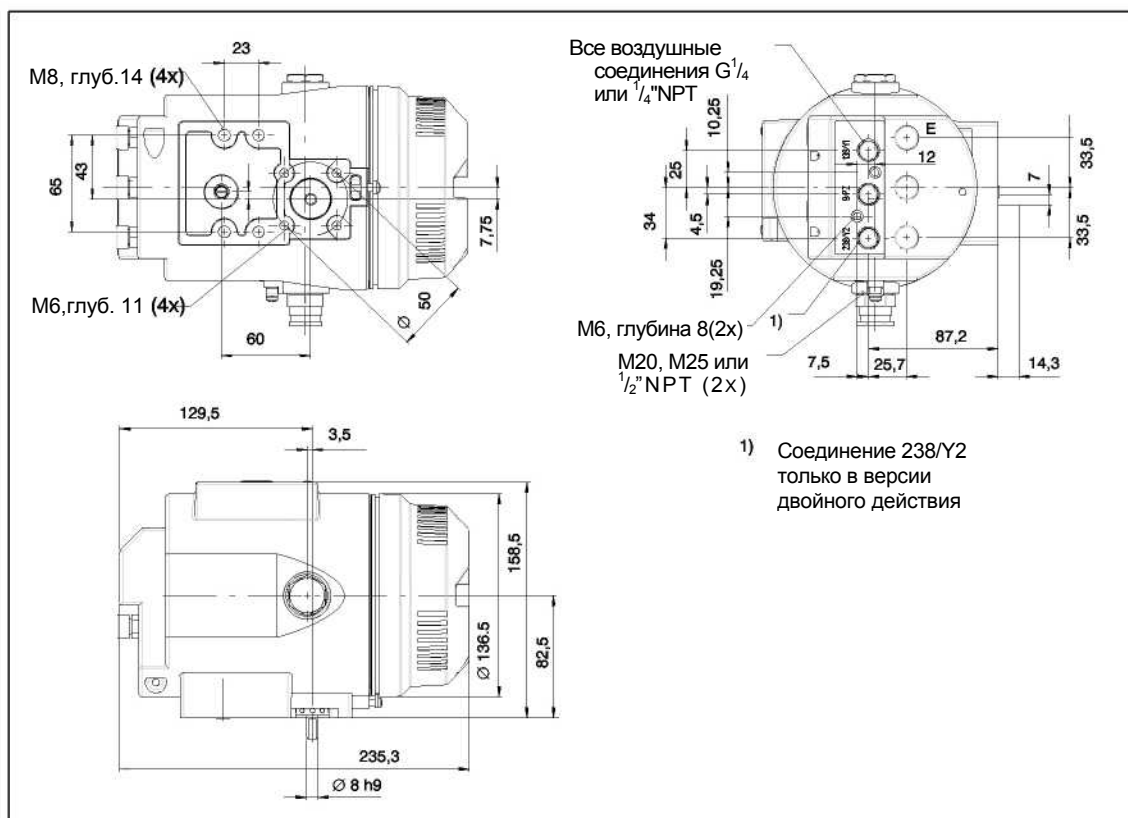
Размерный чертеж позиционера с металлическим корпусом во взрывонепроницаемой версии 6DR5xx5
